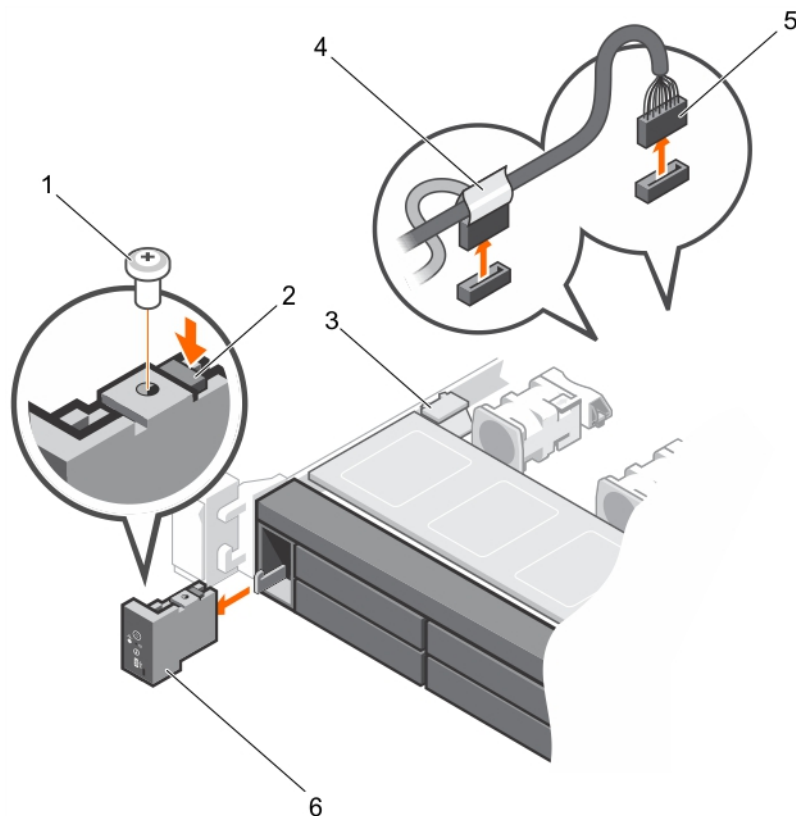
Entfernen des Bedienfelds – Gehäuse für vier 3,5 Zoll-Festplatten
